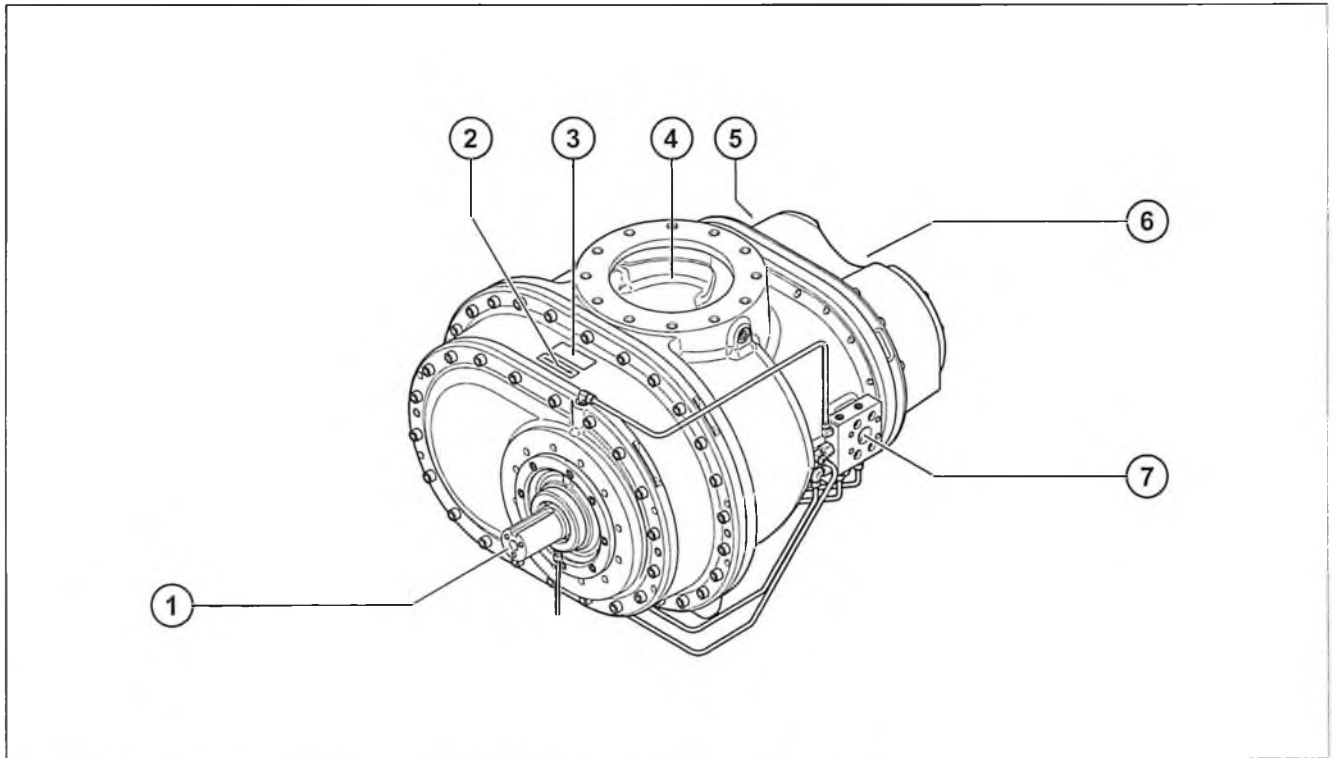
Газовый винтовой компрессорный блок EVO Gas (без редуктора, пример)
